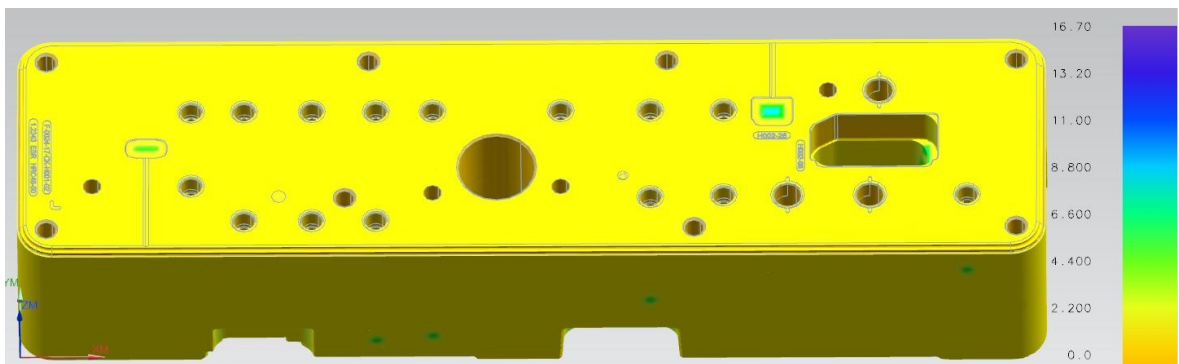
Dráhy vrtání děr o průměru 10,5mm
